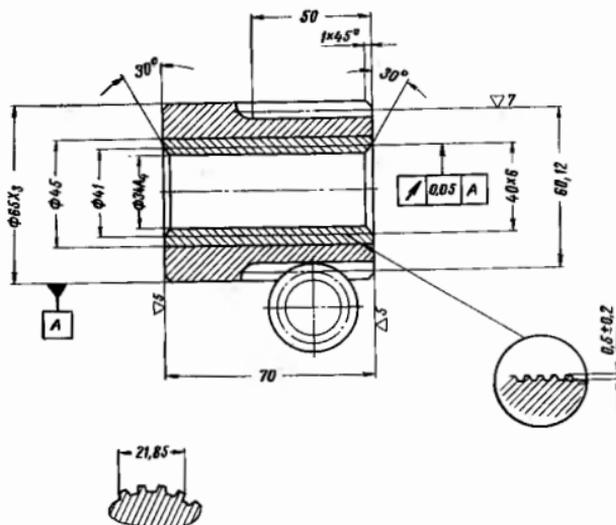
Гайка биметаллическая. Деталь 6М82-7-101
